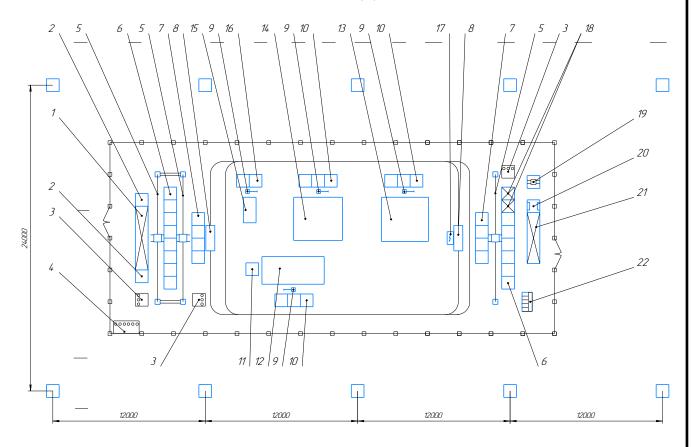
Компоновка ГПО для обработки деталей типа "тел вращения"
